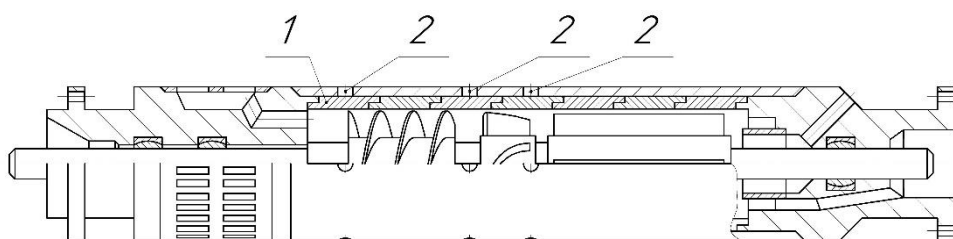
Модернизированный центробежный газосепаратор конструкции П.Д. Ляпкина:
